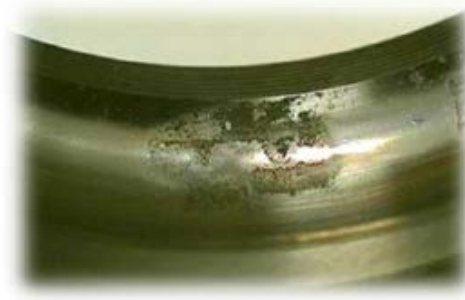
Défaut de roulement – corrosion [6]
